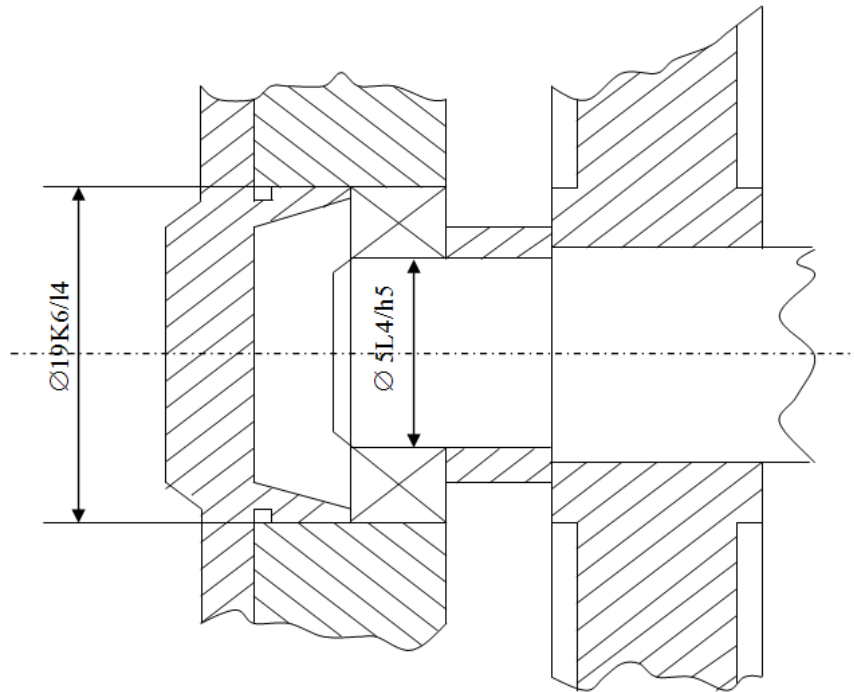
Эскиз сопряжения подшипника с валом и корпусом
